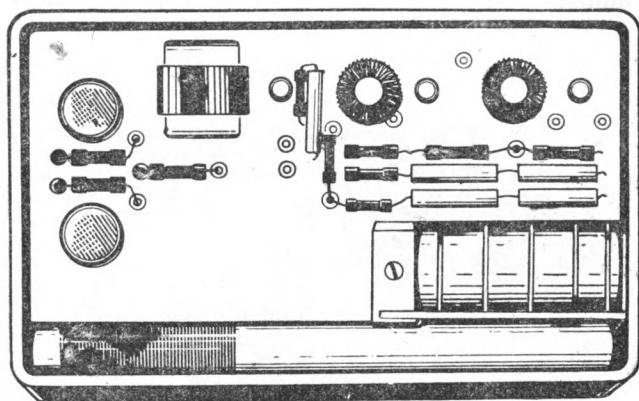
Размещение деталей и внутренний вид приемника прямого усиления
